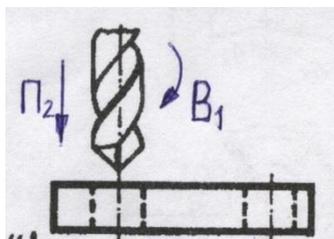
Схема сверления отверстия в прямоугольной заготовке: $B1$ – главное движение – вращение сверла; $P2$ – осевая подача сверла
